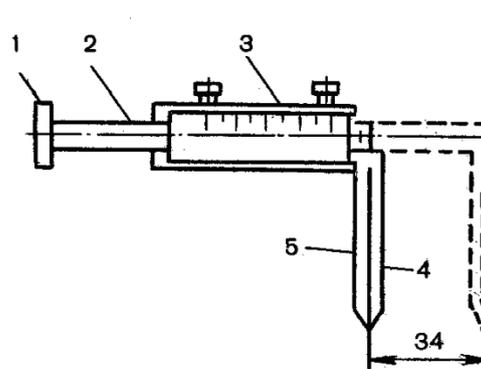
Универсальный измеритель: 1 — стопорное кольцо; 2 — стержень; 3 — обойма; 4, 5 — измерительные губки
